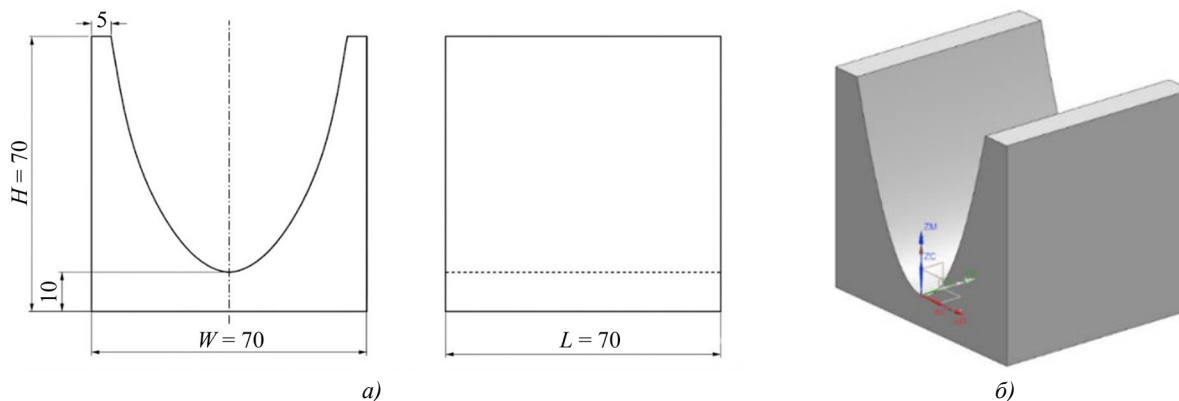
Чертеж экспериментального образца a — двухмерный чертеж; b — трехмерная модель
